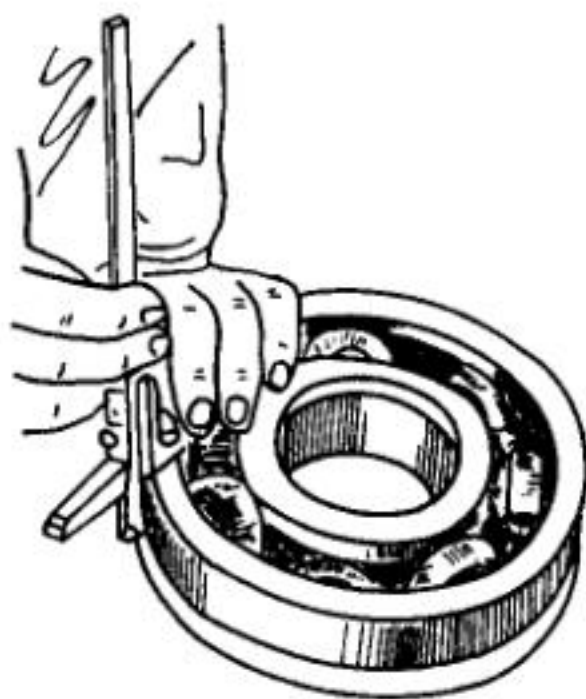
测量后轴承前端面至弹性挡圈内侧的尺寸
